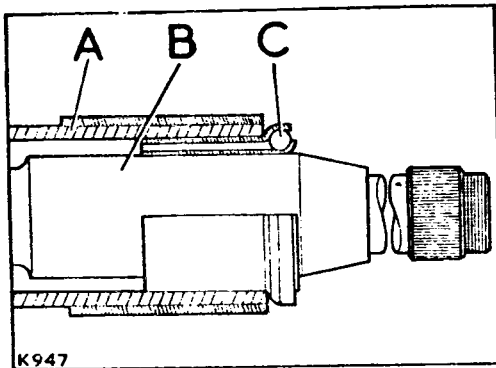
Sección longitudinal de la parte superior de la columna de tipo moderno.
